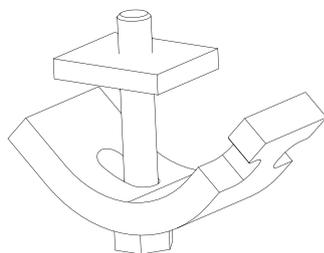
Griffes de serrage, anti-torsion, épaisseur de serrage 6-25 mm (acier galvanisé)
